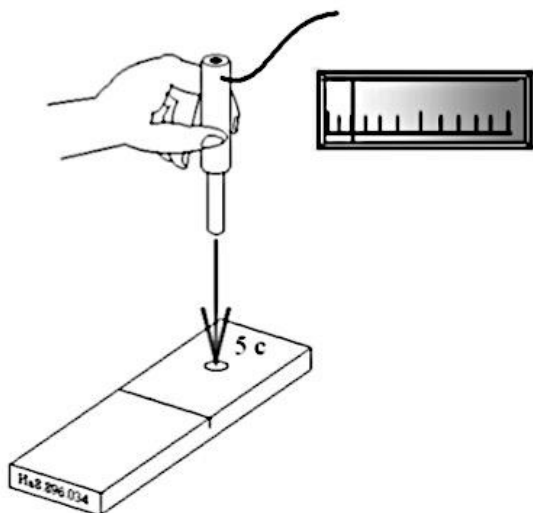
Балансировка измерительной схемы с установкой рабочего нуля [20]
